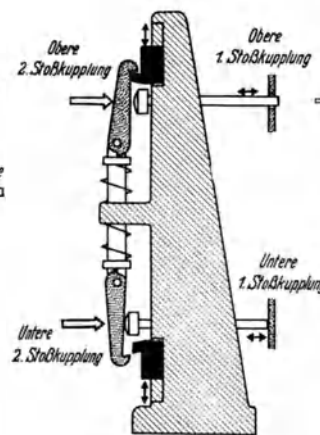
Grundgetriebe einer Schafmaschinensteuerung für Seidenstühle (Zwillings-Schaftsteuerung.)
